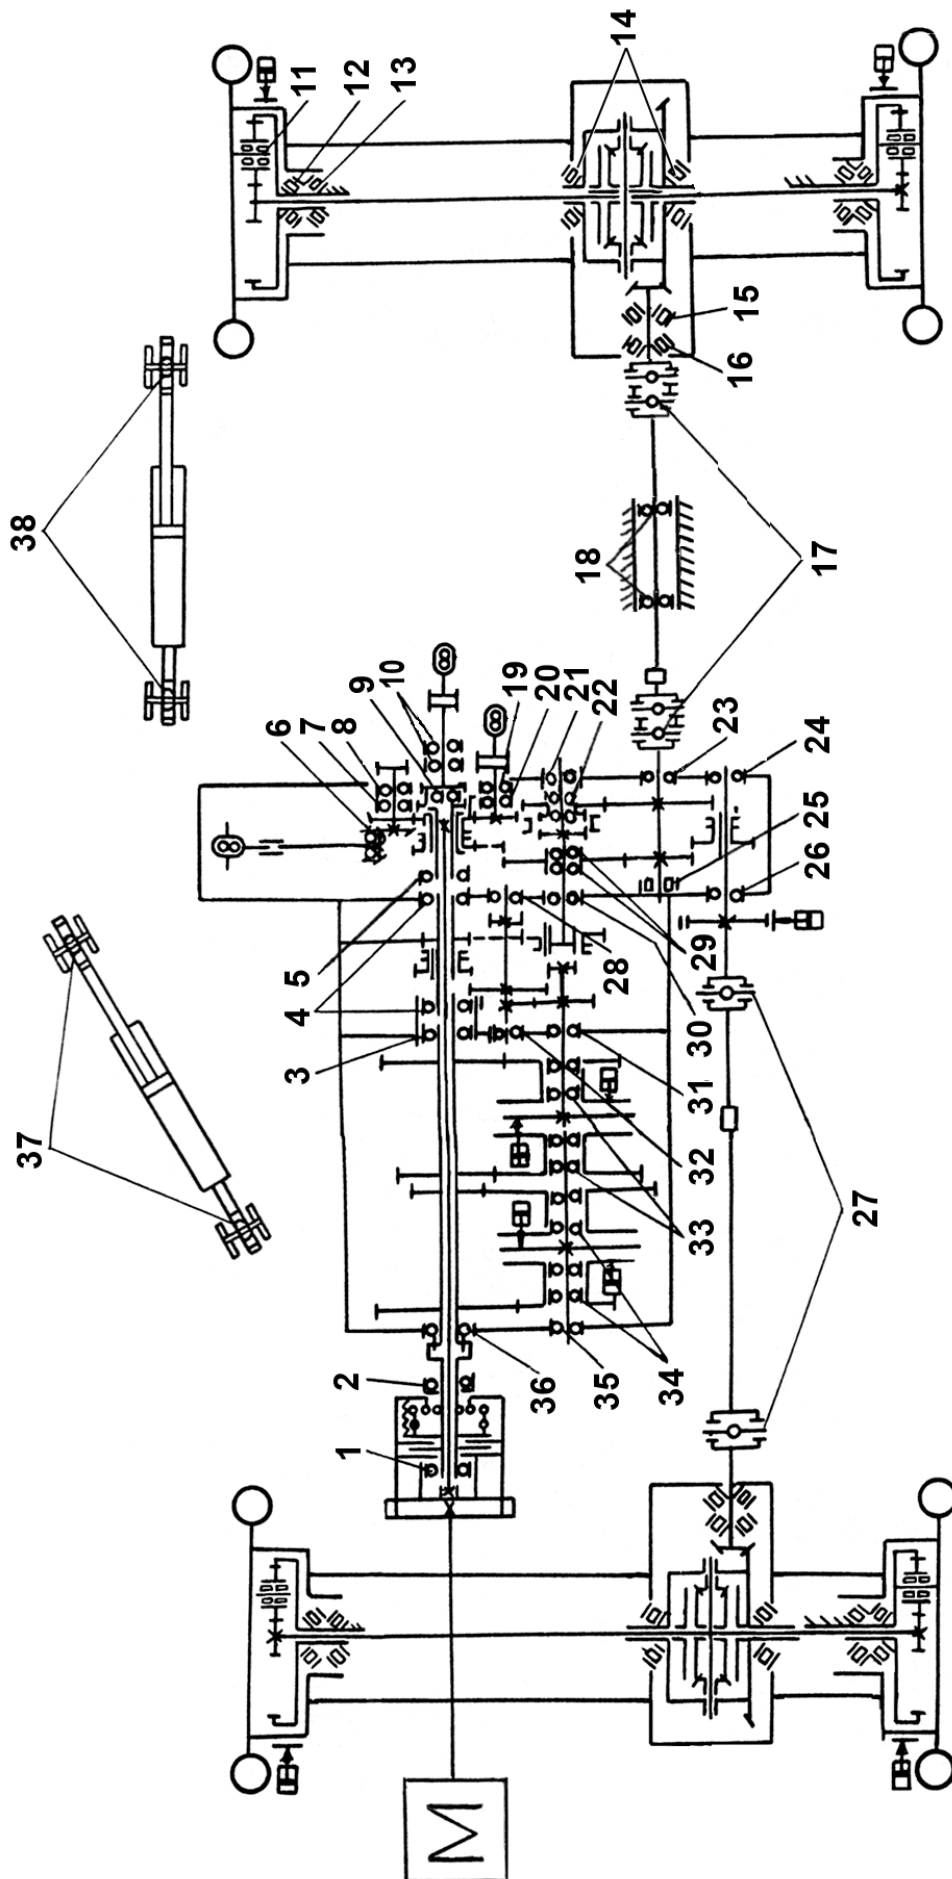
Схема расположения подшипников на тракторе-погрузчике
